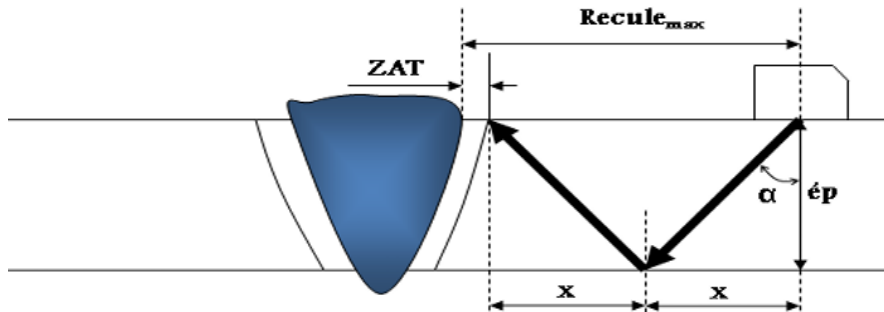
Inspection ultrasonore d'une soudure
